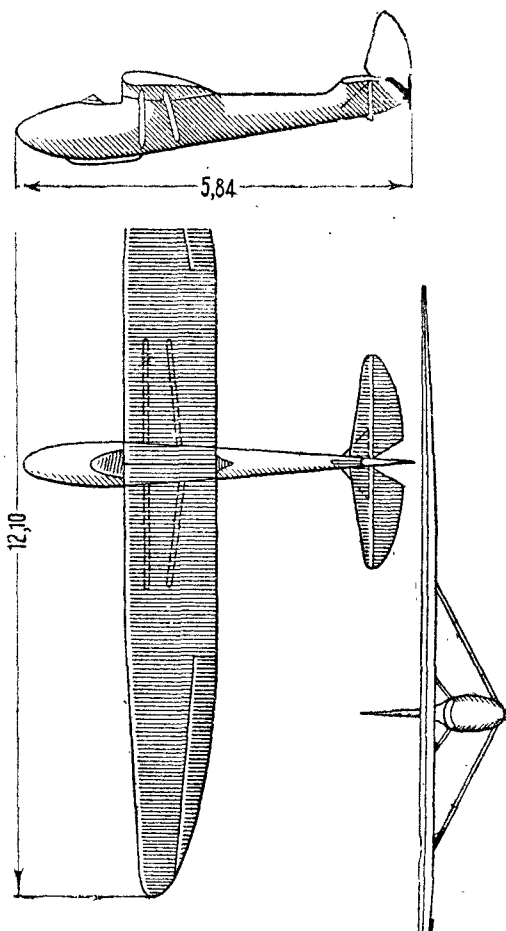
Схема рекордного планера ГН-7 конструкции Грошева (вид сверху, сбоку и спереди).
